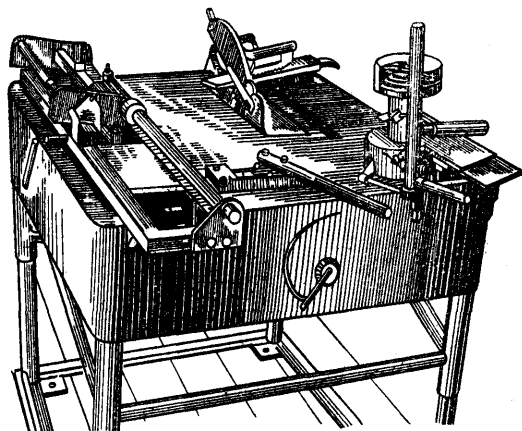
Универсальный станок треста Отделстрой для обработки паркета.
